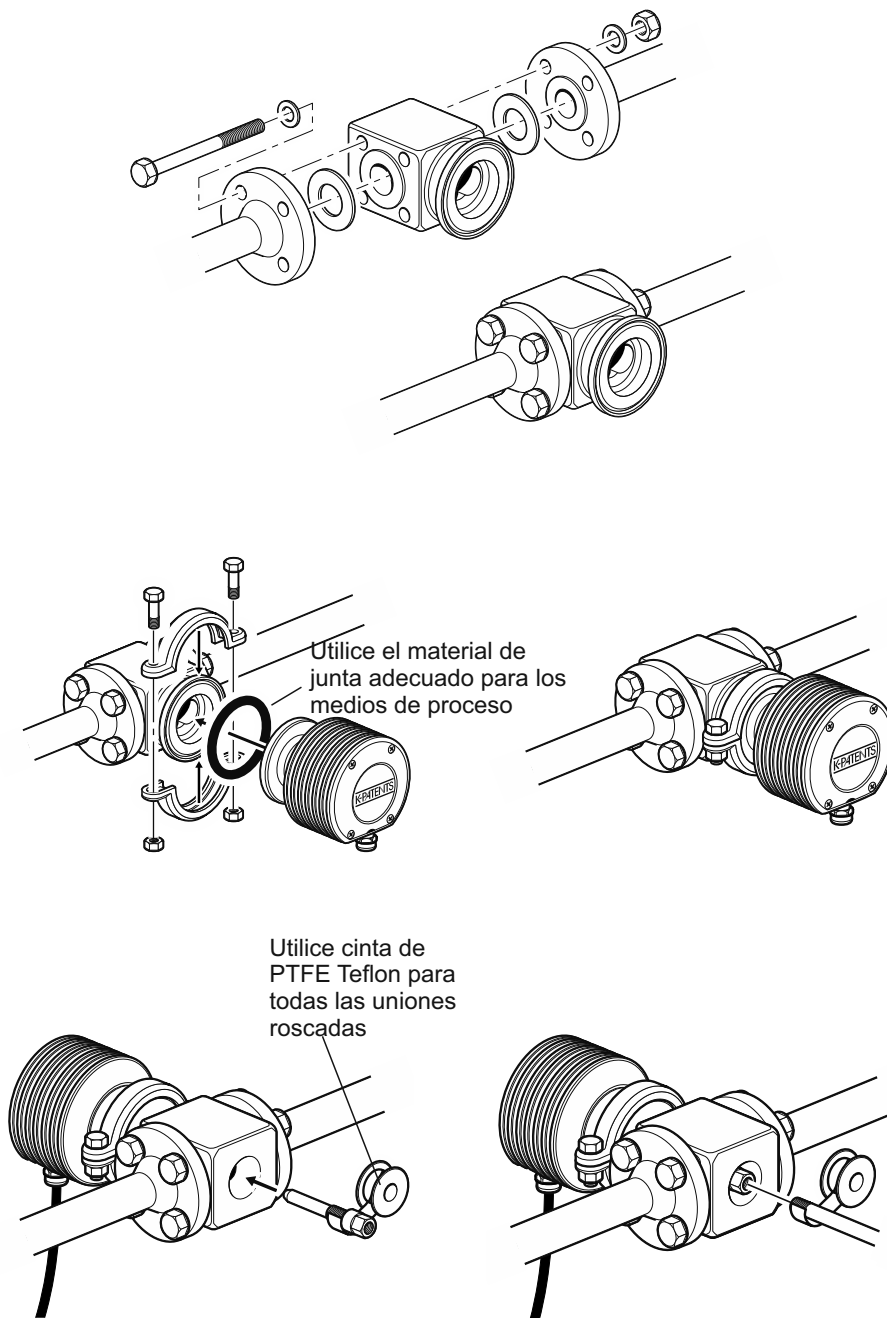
Montaje de la célula de flujo de placa de contactos y del sensor en una tubería horizontal
